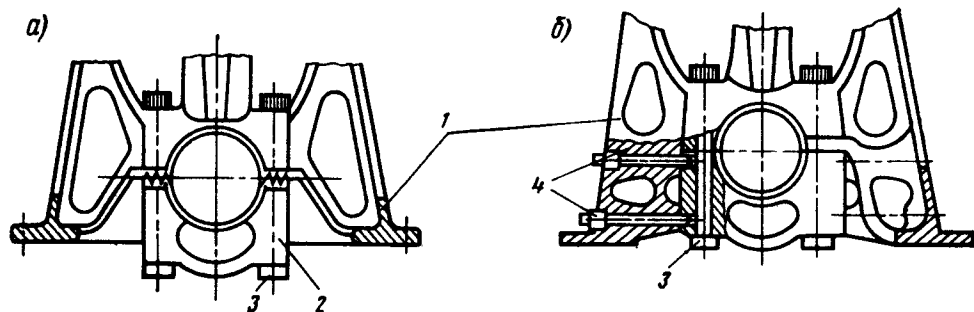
Варианты соединения подвесок коренных подшипников со стойками дизеля: а — с зубчатым стыком; б — с плоским; 1 — стойка дизеля; 2 — подвеска; 3, 4 — болты крепления
